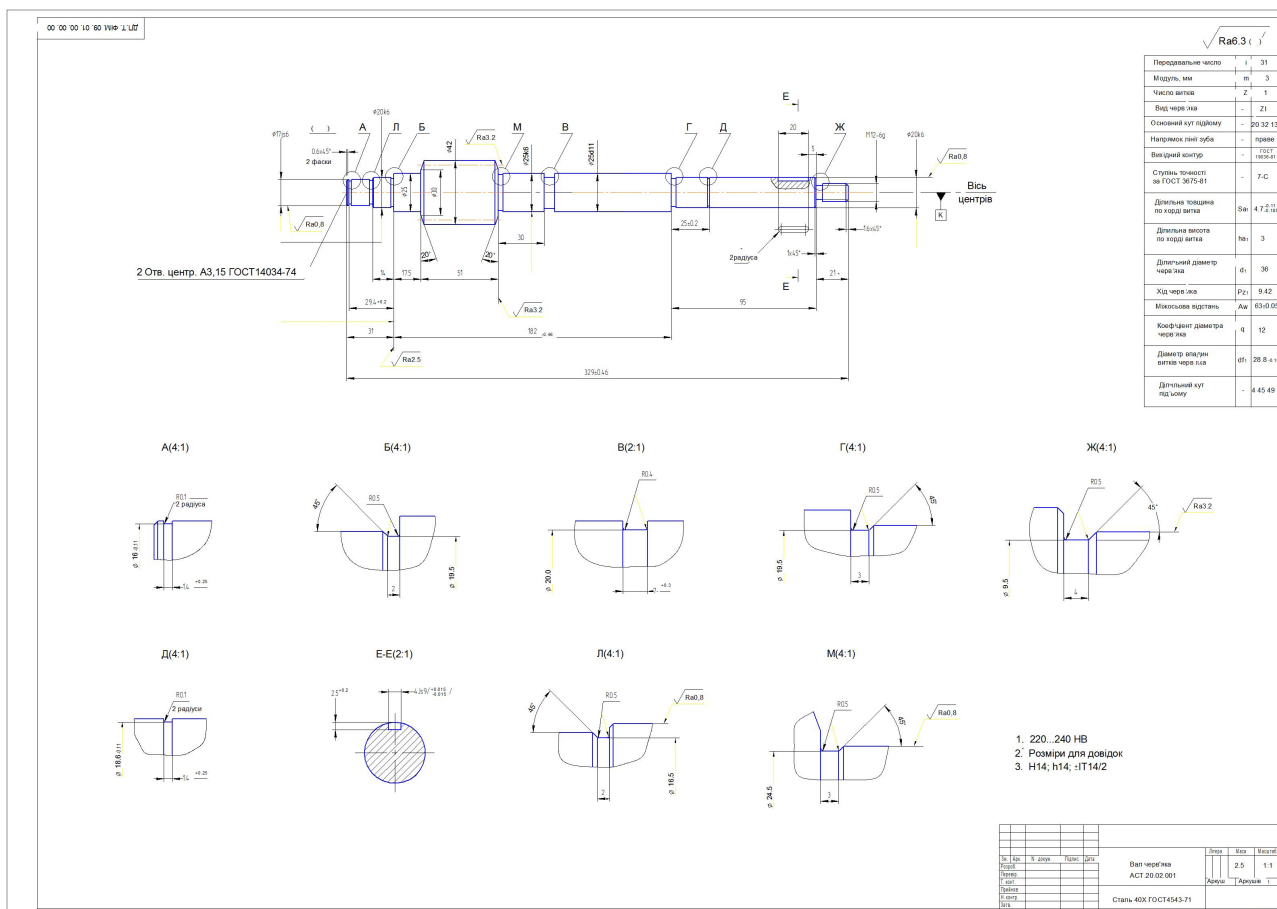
Креслення вала черв'яка АСТ 20.02.001
